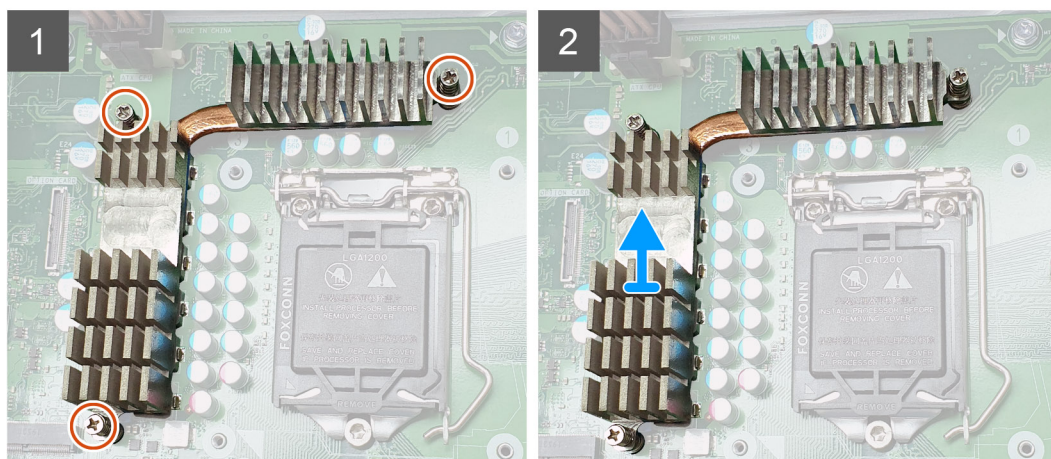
Assemblage du dissipateur de chaleur du régulateur de tension sur un système équipé d'un processeur 125 W
